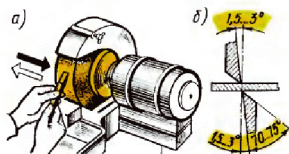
Заточка режущих инструментов на станке ИЭ-9703В (а) и углы их заточки (б)
